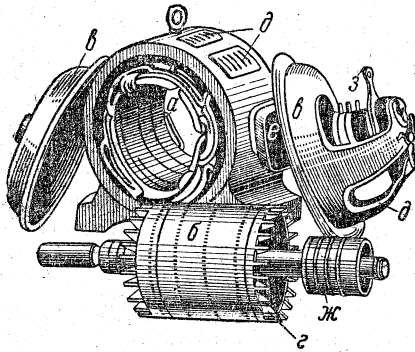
Асинхронный двигатель с контактными кольцами в разобранном виде.
